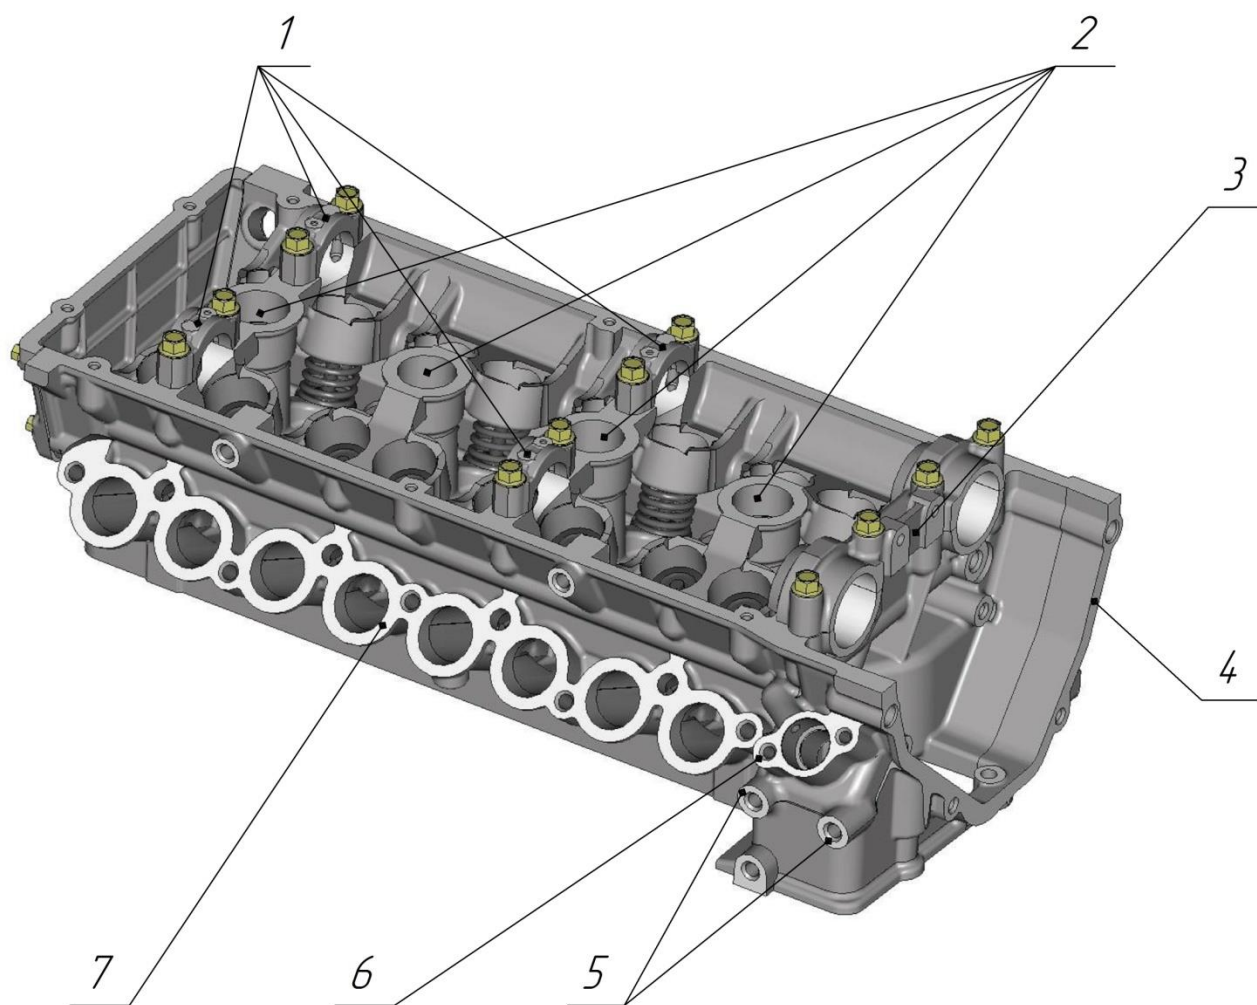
Головка цилиндров. Вид на фланец впускной трубы, на верхнюю плоскость и на фланец передней крышки:
